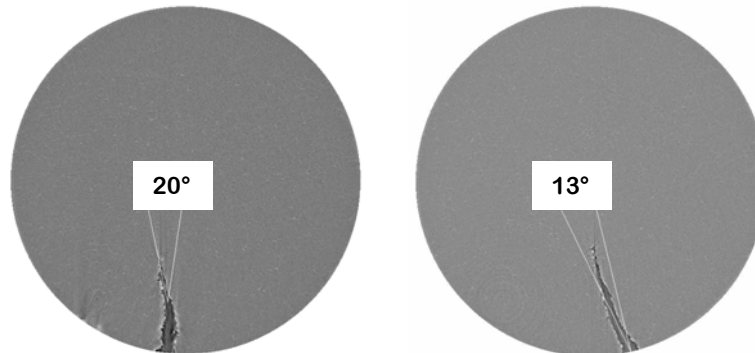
Slices a -0.7 mm e $+0.7$ mm rispetto alla sezione di minor diametro.
